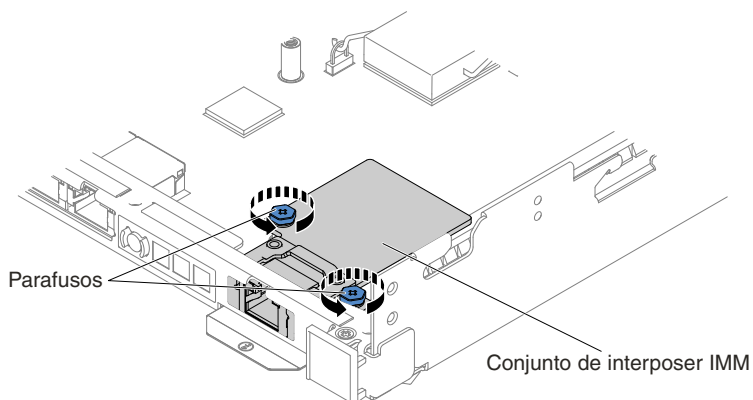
Parafusos soltos do conjunto de cabo adaptador de IMM
